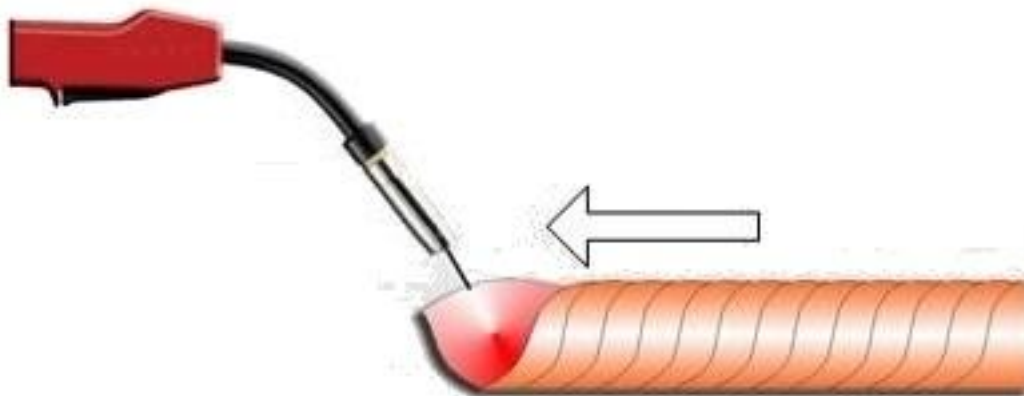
Схема процесса механизированной сварки углом назад
